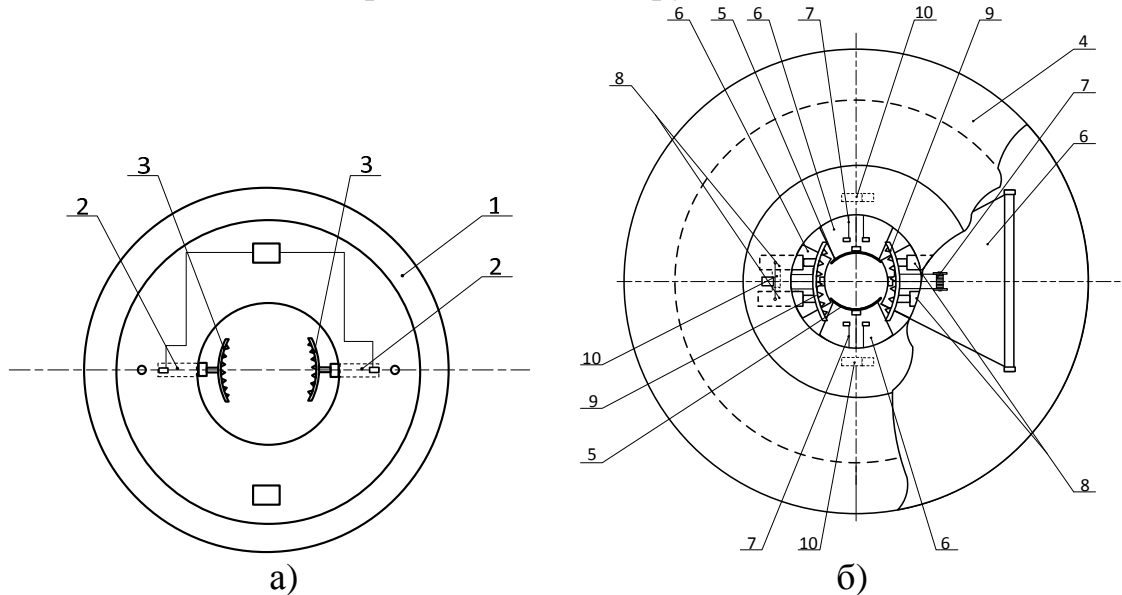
Вид разделяющегося грузозахватного механизма сверху: а) верхний узел; б) нижний узел
